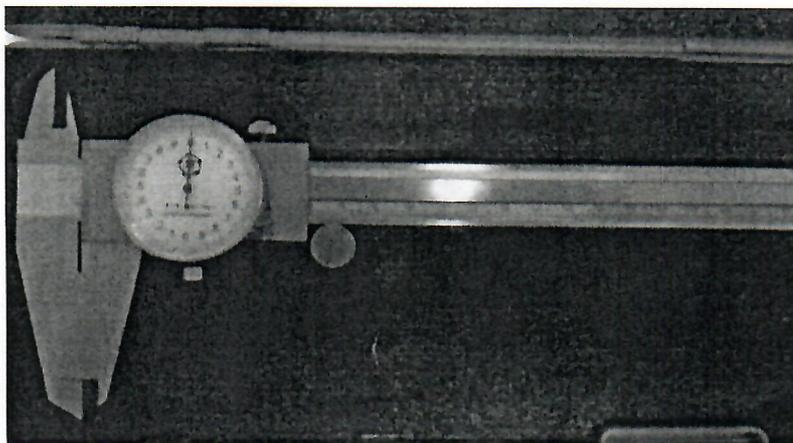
Общий вид штангенциркулей типа ШЦК-I.
